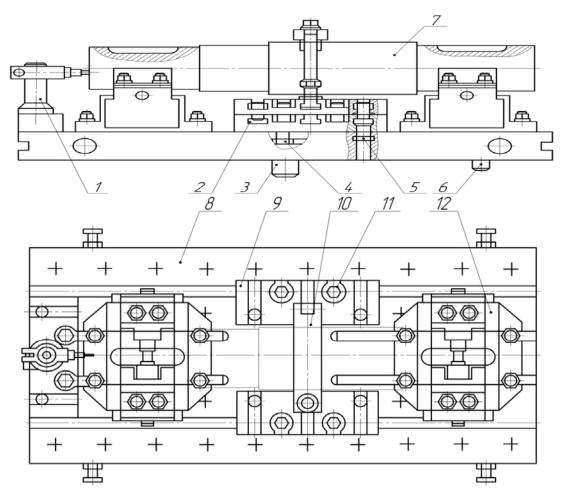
Сборно-разборное приспособление (СРП – ЧПУ) для установки вала: 1 – опора; 2, 3 – базирующие пальцы; 4 – пазовый болт; 5, 6 – базирующие пальцы; 7 – заготовка; 8 – плита; 9 – планка; 10 – прижим; 11 – гайка; 12 – призма
